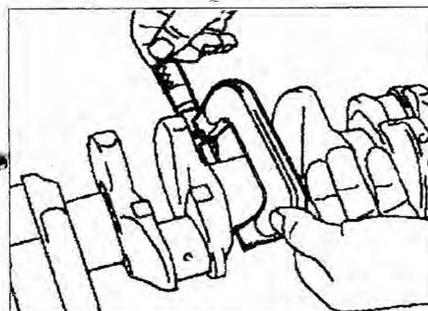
Измерение диаметра шейки коренного подшипника.
